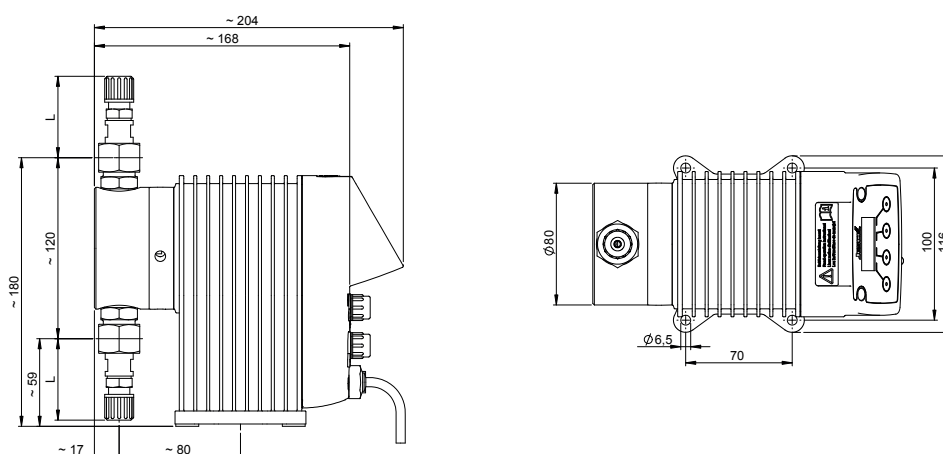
Габаритный чертеж MAGDOS LA / LD с дозирующей головкой из нержавеющей стали (1.4571) (все размеры в мм)
